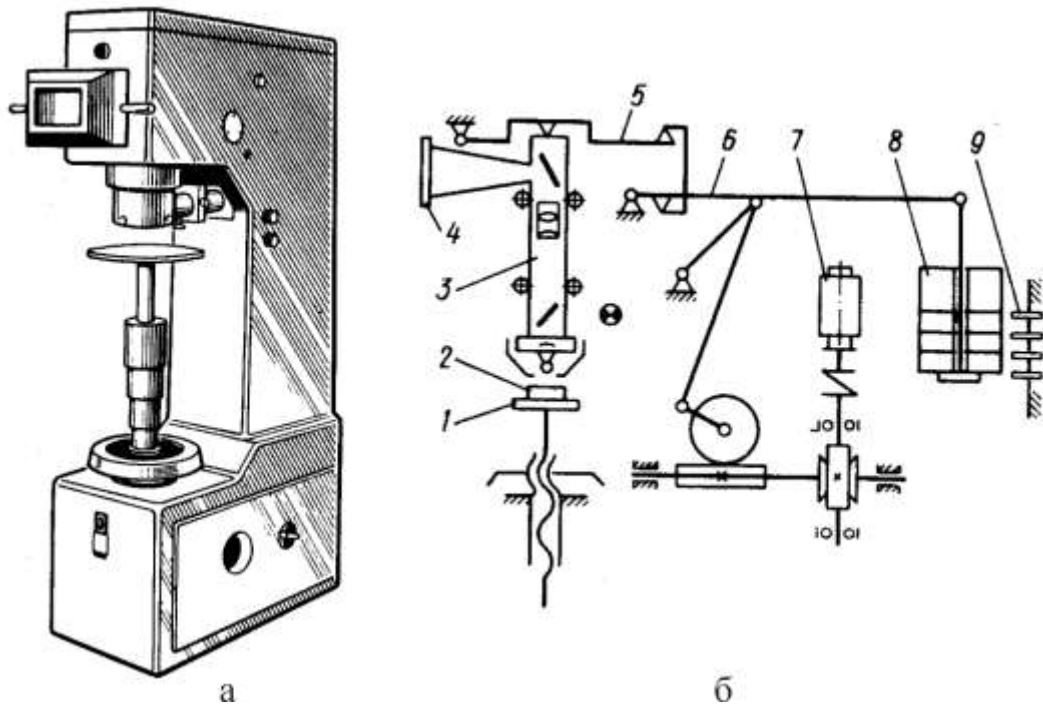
Прилад БТБ-11-3 для вимірювання твердості за методом Бринелля: а – загальний вигляд; б – схема випробовування зразка: 1 – столик; 2 – контрольований зразок; 3 – шпindel; 4 – екран; 5, 6 – ва-желі; 7 – електродвигун з редуктором; 8 – вантажі; 9 – штирі
